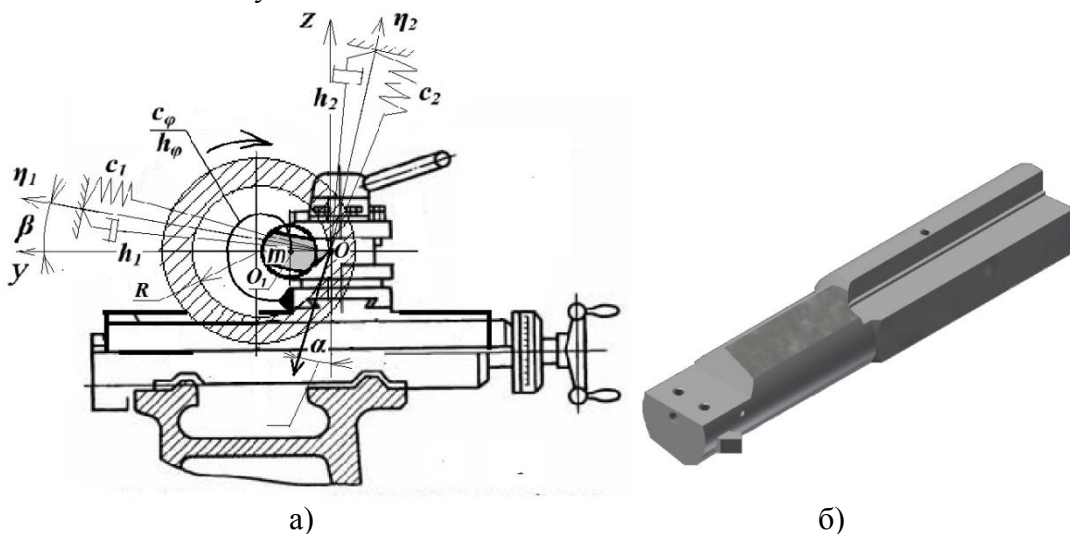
Розрахункова схема процесу розточування на токарно-гвинторізному верстаті (а) та загальний вигляд модернізованої конструкції розточувальної оправки (б)
